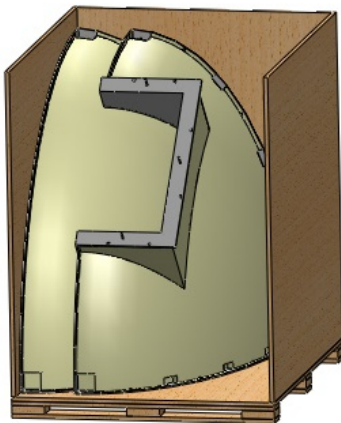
Vista de la ubicación de la cúpula dentro de la caja de embalaje.
